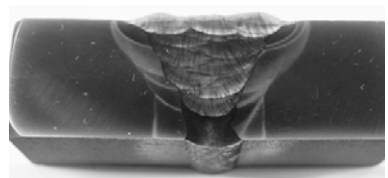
Загальний вигляд зварного з'єднання, положення 2G
